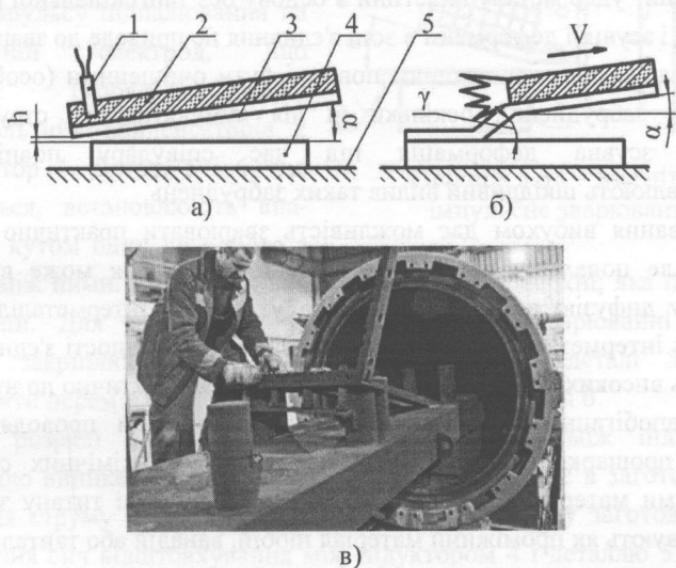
Кутова схема зварювання вибухом до початку (а) і в стадії вибуху (б), а також загальний вигляд камери для зварювання (в)
